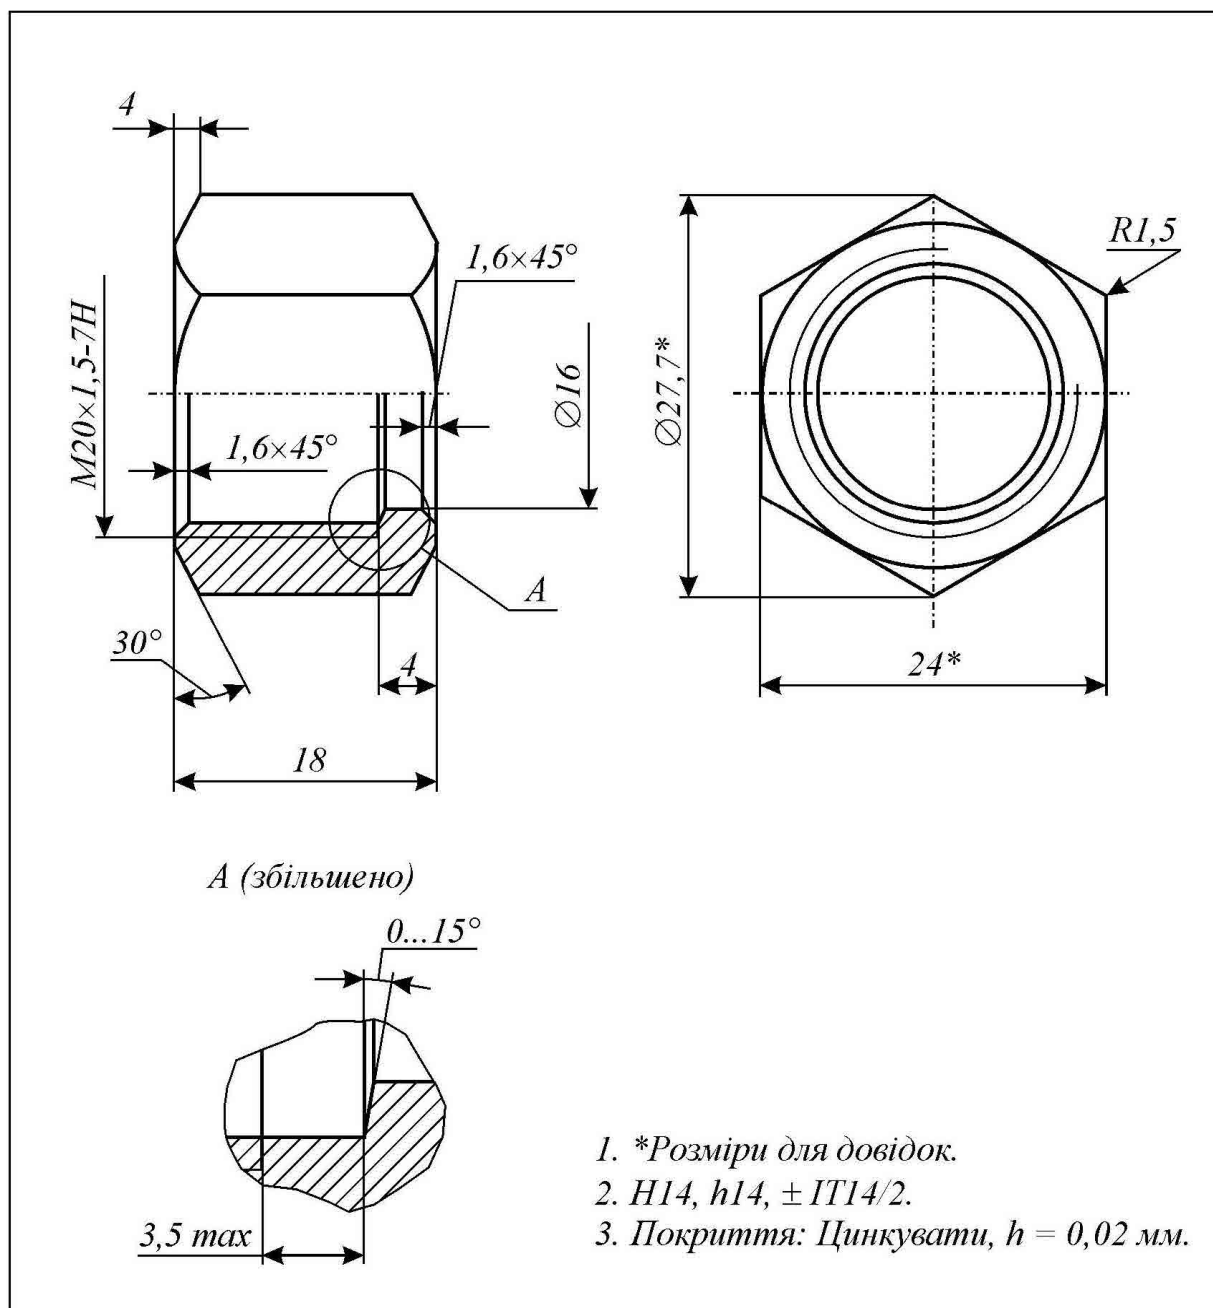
Фрагмент кресленика деталі «Гайка накидна»
